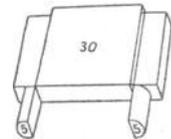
Meßschnäbel für Lochmessung mittels Endmaßen.
